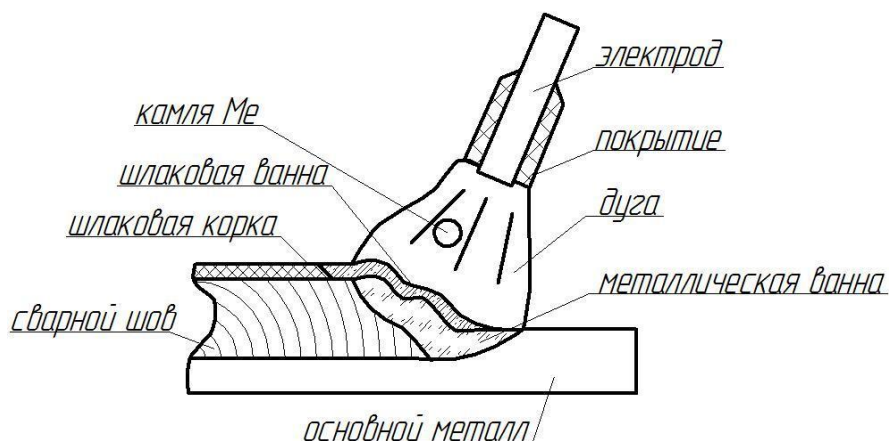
Ручная дуговая сварка покрытыми электродами
